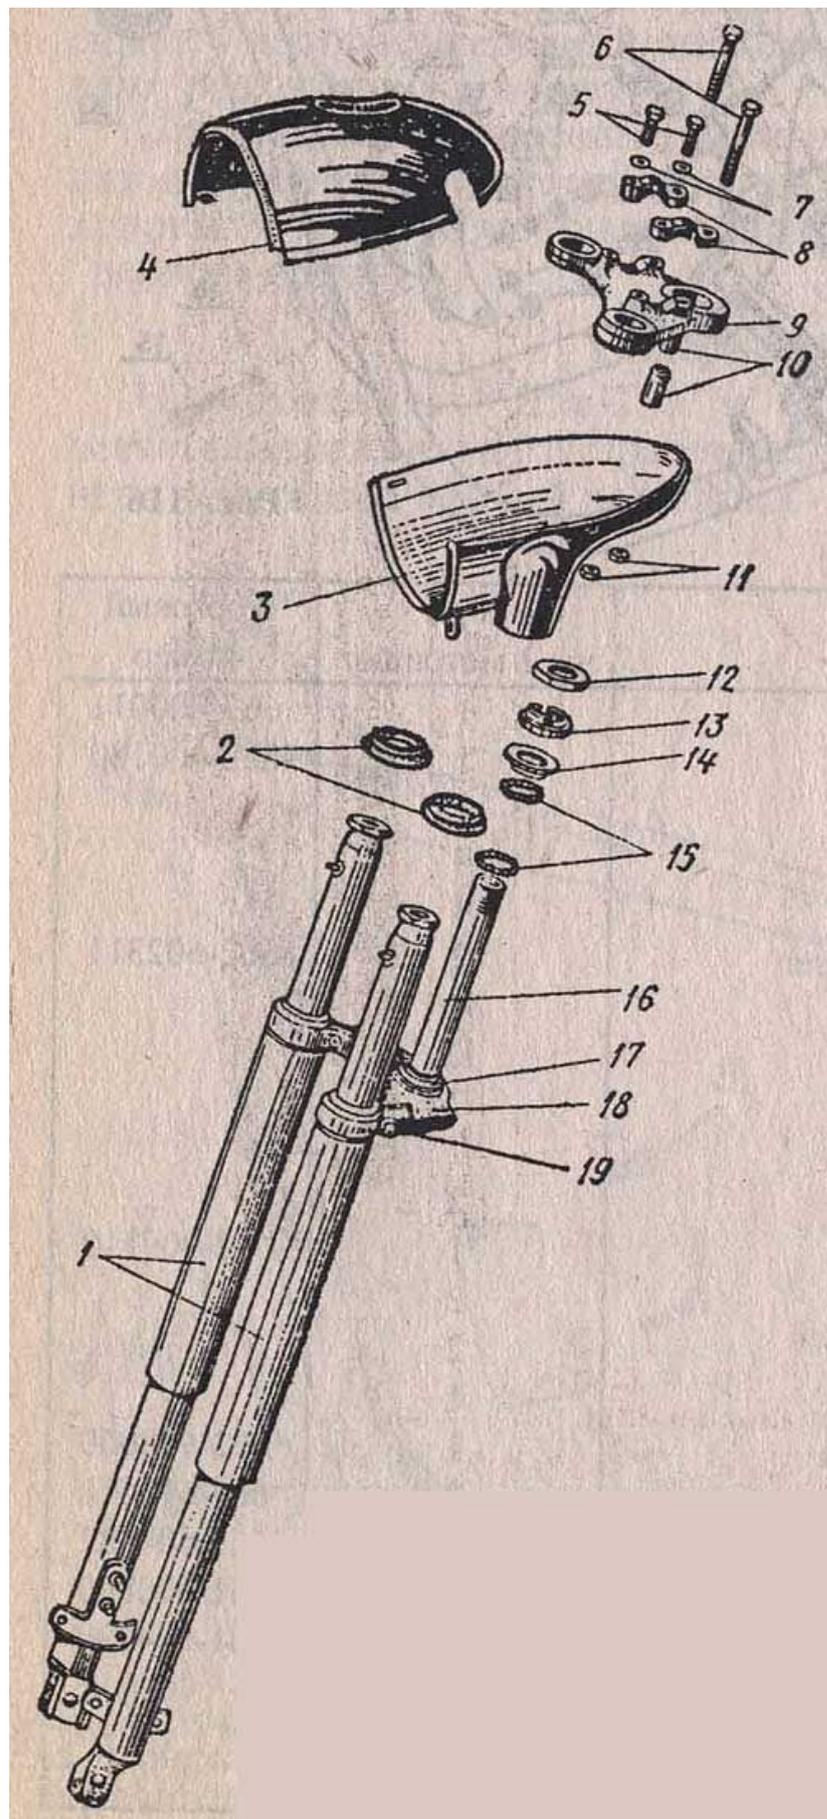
Передняя вилка и детали рулевой колонки (без рулевой головки рамы) ранних выпусков: 1 - перья вилки; 2 - резиновые прокладки; 3 и 4 - нижний и верхний кожухи
